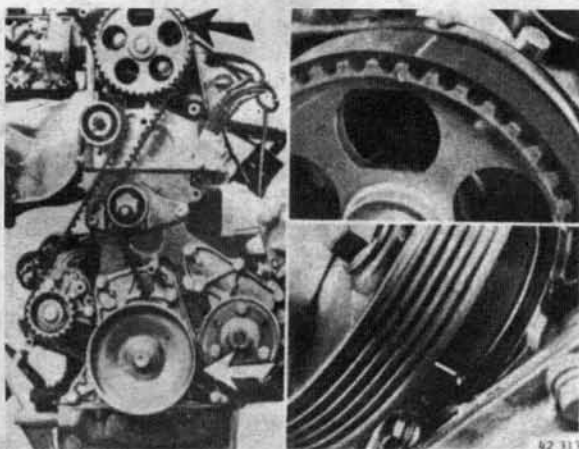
Установка зубчатого ремня привода механизма газораспределения. Правильное расположение элементов привода
